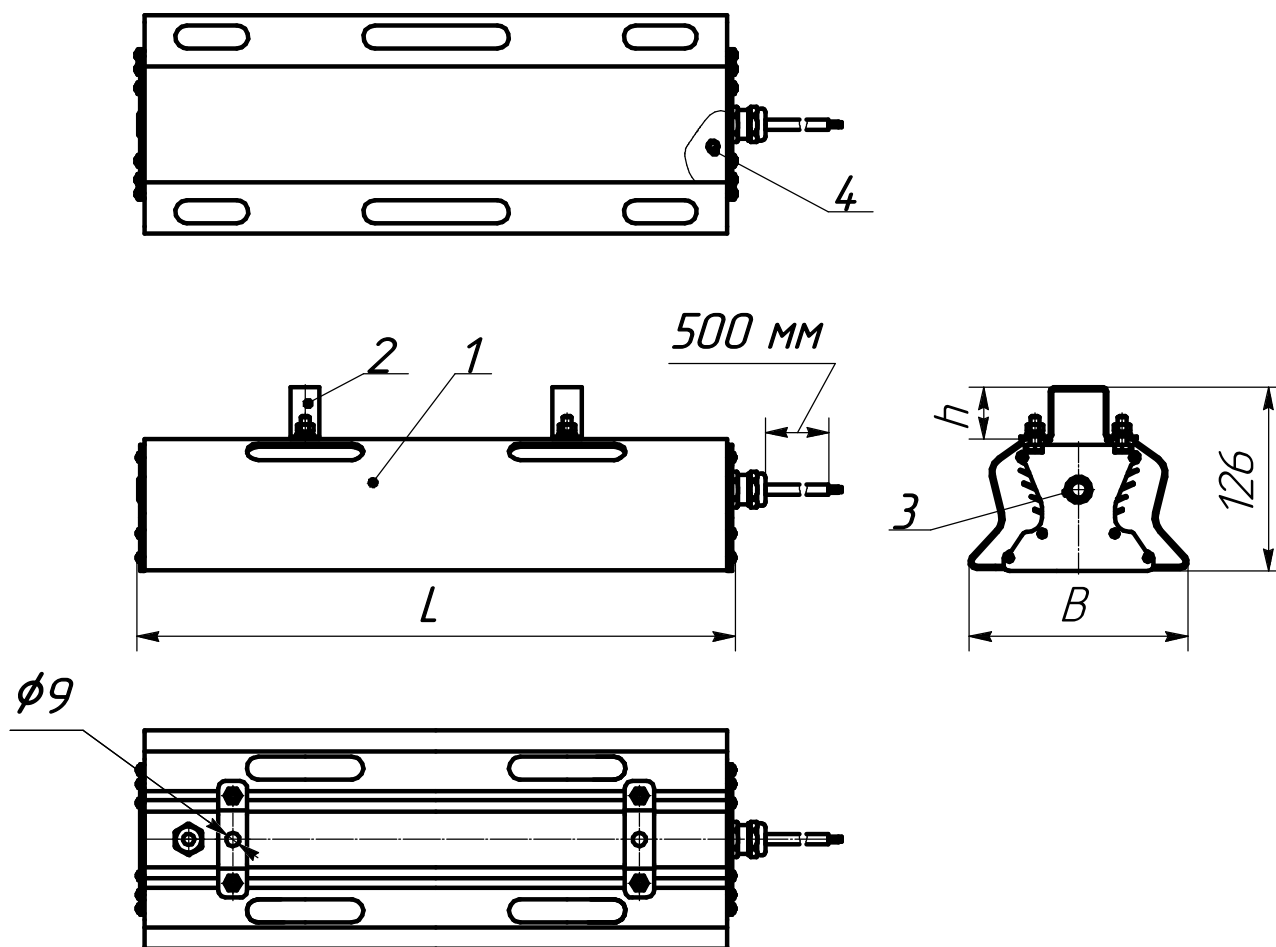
Внешний вид и габаритные размеры светильников ДСП97
